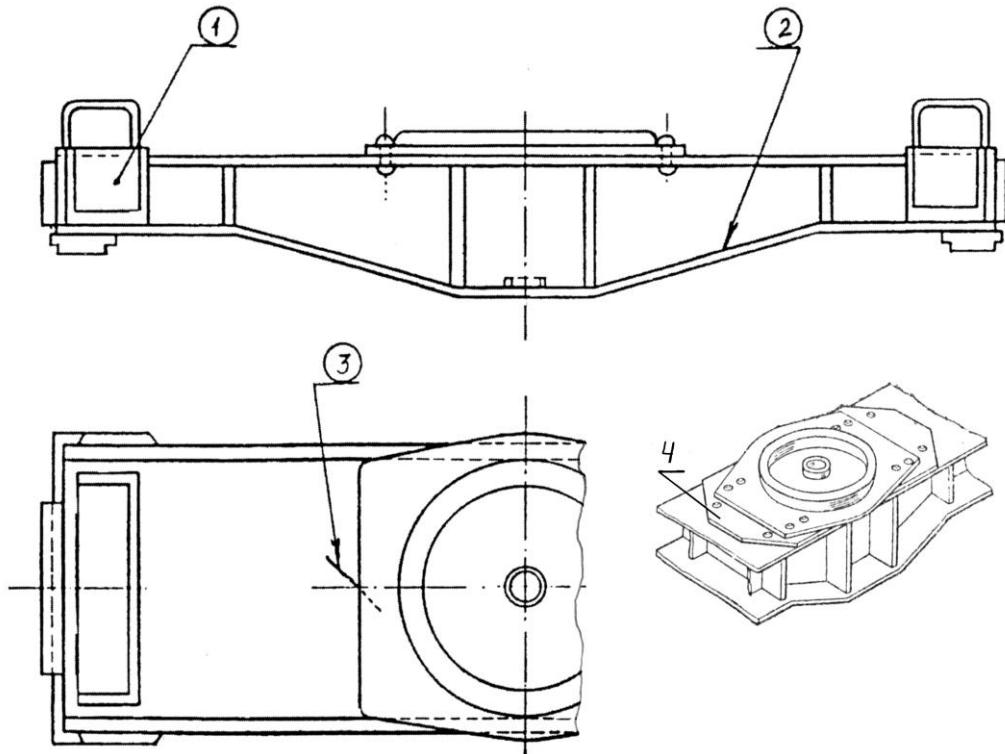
Основные дефекты балки надрессорной сварной тележки ЦМВ, ремонтируемые сваркой или наплавкой
